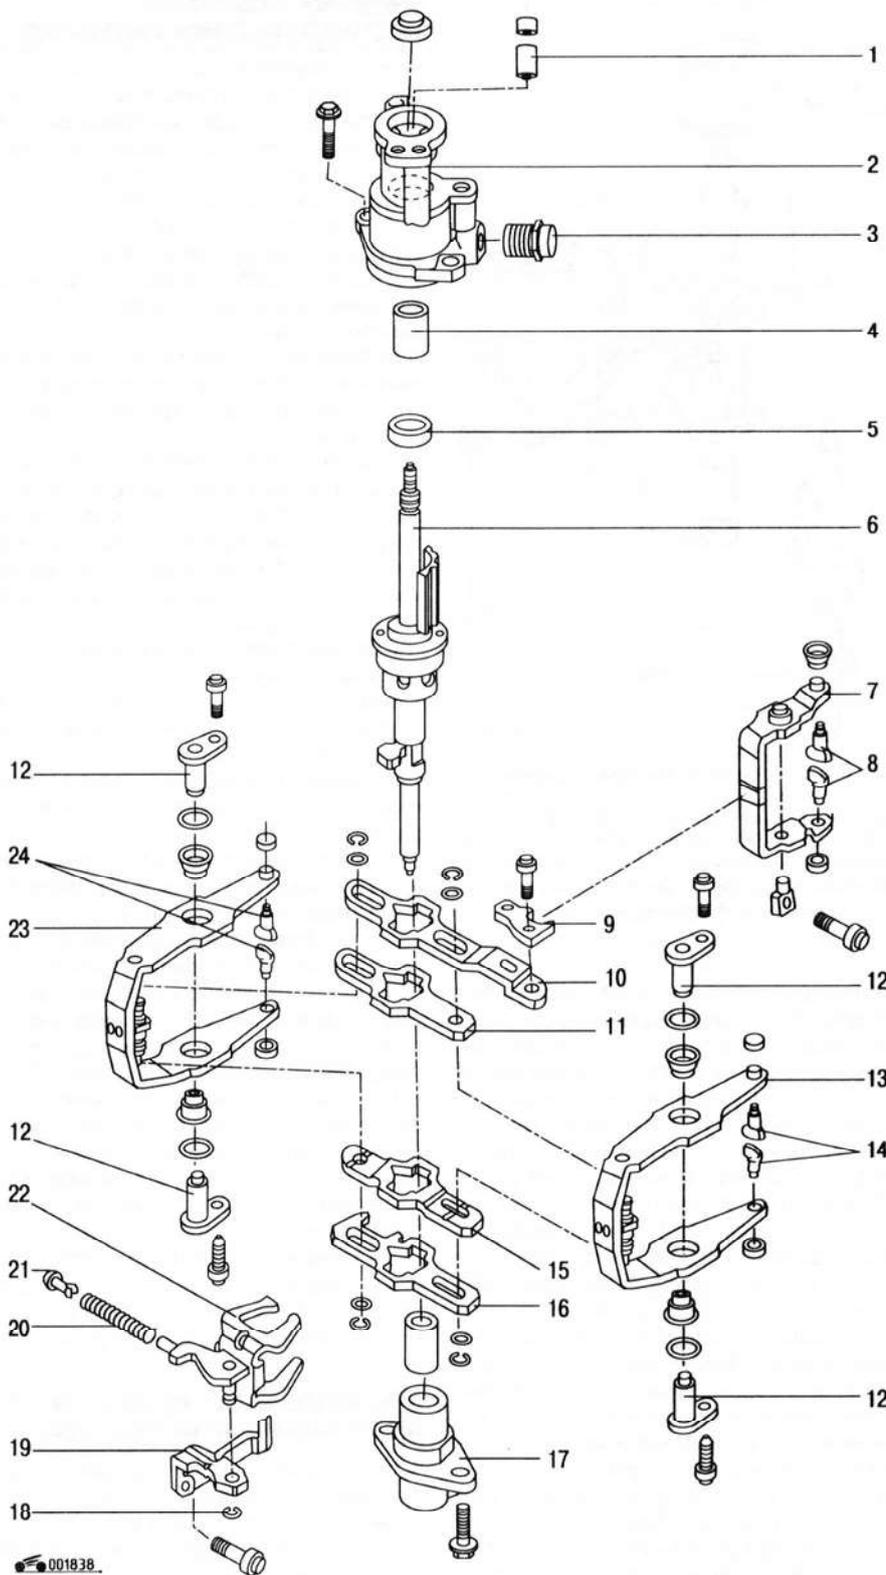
Механизм переключения передач: 1 – втулка; 2 – корпус; 3 – стопорный винт; 4 – опорная втулка; 5 – уплотнительное кольцо; 6 – вал механизма выбора передач; 7 – вилка включения V передачи; 8 – наконечник вилки включения V передачи; 9 – рычаг включения V передач; 10 – рычаг вилки включения V передачи; 11 – рычаг вилки включения III и IV передач; 12 – цапфа вилки включения передач; 13 – вилка включения III и IV передач; 14 – наконечник вилки включения III и IV передач; 15 – рычаг вилки включения I и II передач; 16 – рычаг вилки включения передачи заднего хода; 17 – опора вала; 18 – стопорное кольцо; 19 – держатель вилки включения передачи заднего хода; 20 – пружина; 21 – штифт; 22 – вилка передачи заднего хода; 23 – вилка включения I и II передач; 24 – наконечник вилки включения I и II передач
